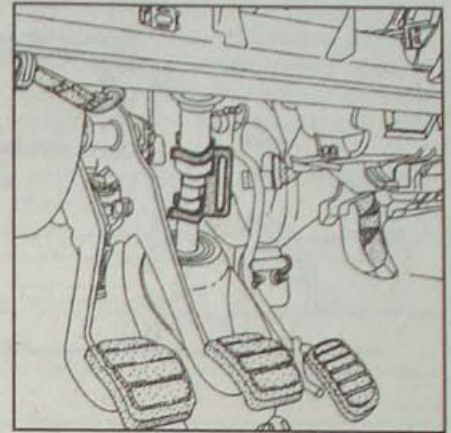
Установка приспособления Dir. 1408 для регулировки положения вилки карданного шарнира рулевого вала относительно приводной шестерни рулевой передачи
